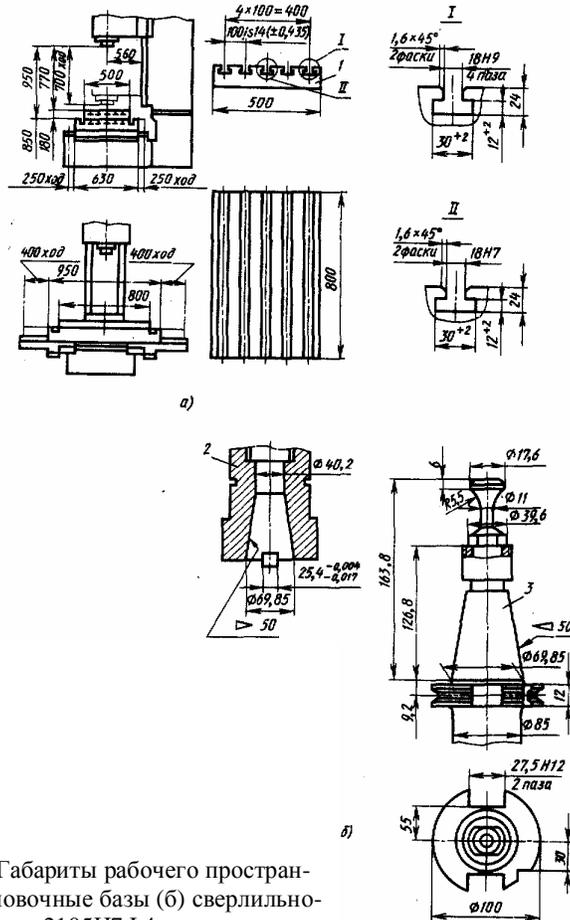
Габариты рабочего пространства (а) и установочные базы (б) сверлильно-фрезерного станка 2105Н7Ф4 (1 – стол; 2 – шпиндель; 3 – оправка)
